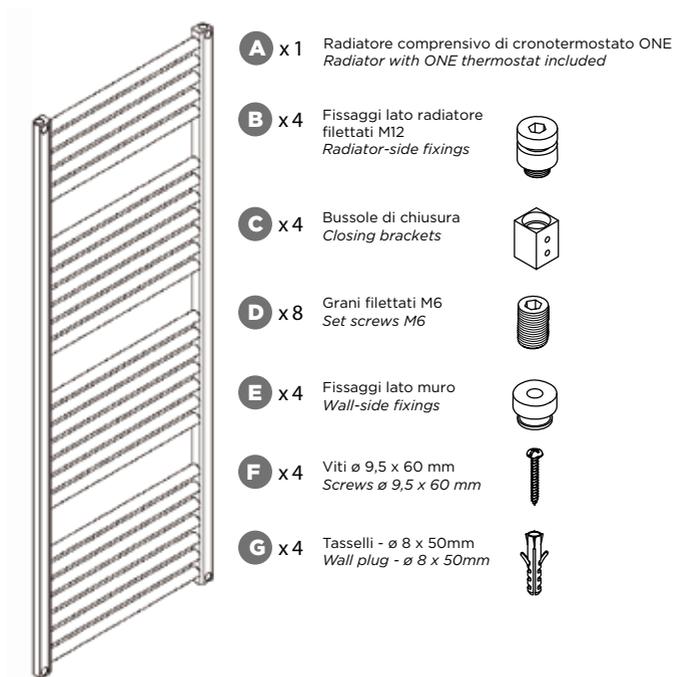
Necessario per l'assemblaggio/Necessary for assembly
